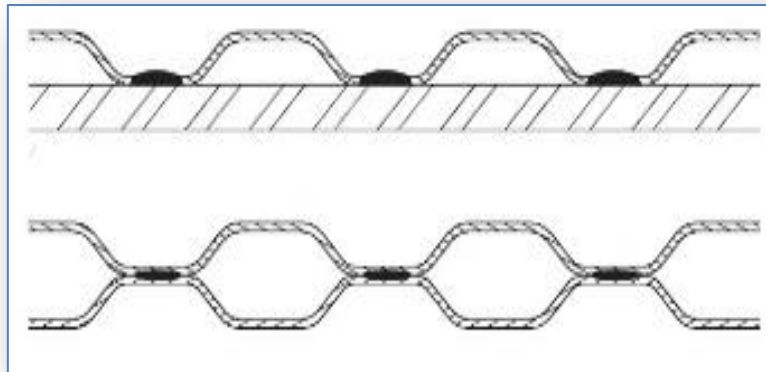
Echangeur de chaleur a plaques soudées
